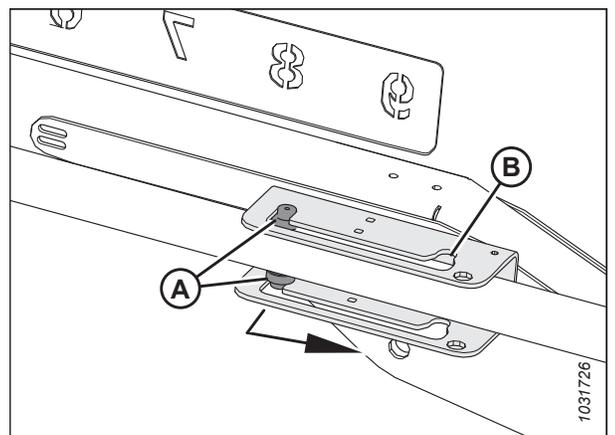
Cilindro del braccio sinistro – Posizione avanzata
